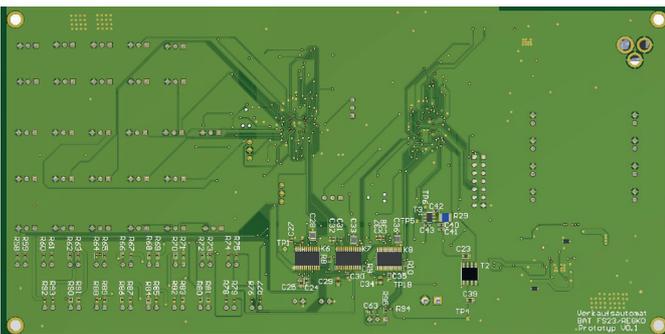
Steuerplatine in der Bottom-View Ansicht.
